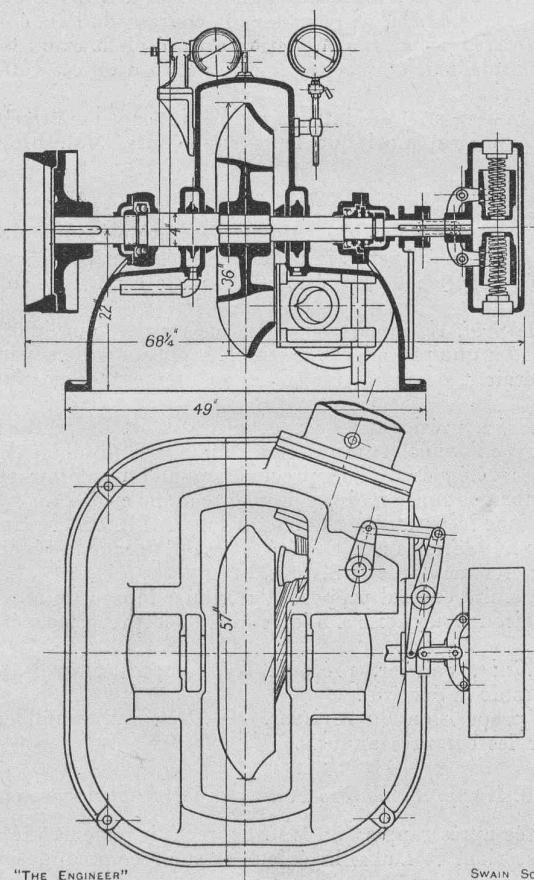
Coupe et plan d'une turbine « Turgo »
